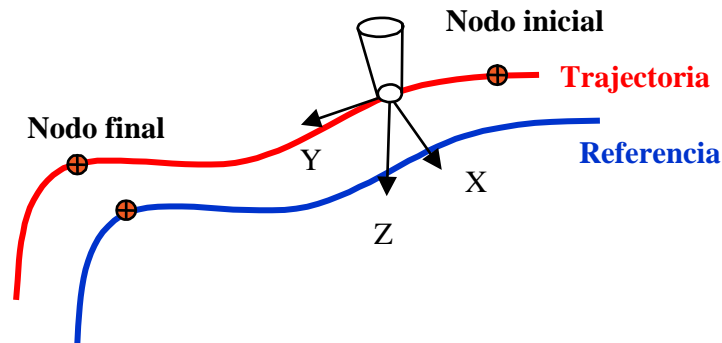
Líneas de trayectoria y referencia de soldadura
